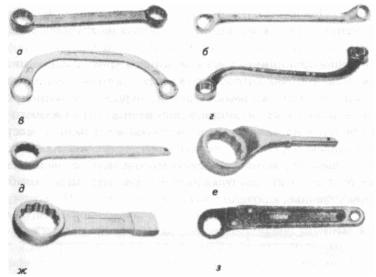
Накидные гаечные ключи: a — двусторонний с отгибом колец 15° ; δ — двусторонний «коленчатый»; ϵ — двусторонний стартерный; ϵ — двусторонний S — образный; δ — односторонний; ϵ — односторонний с разъемным кольцом; ϵ — двусторонний с храповыми механизмами
